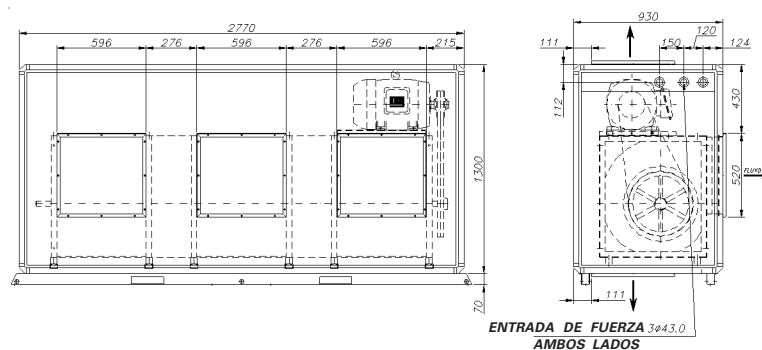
Dimensiones Módulo Ventilador 125 a 300
